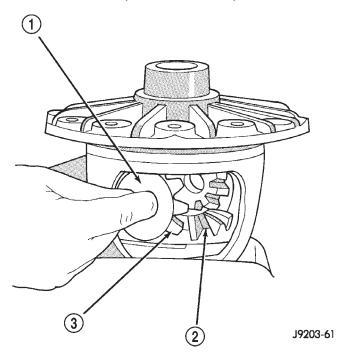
ENGRANAJE HERMANADO DEL PIÑON
